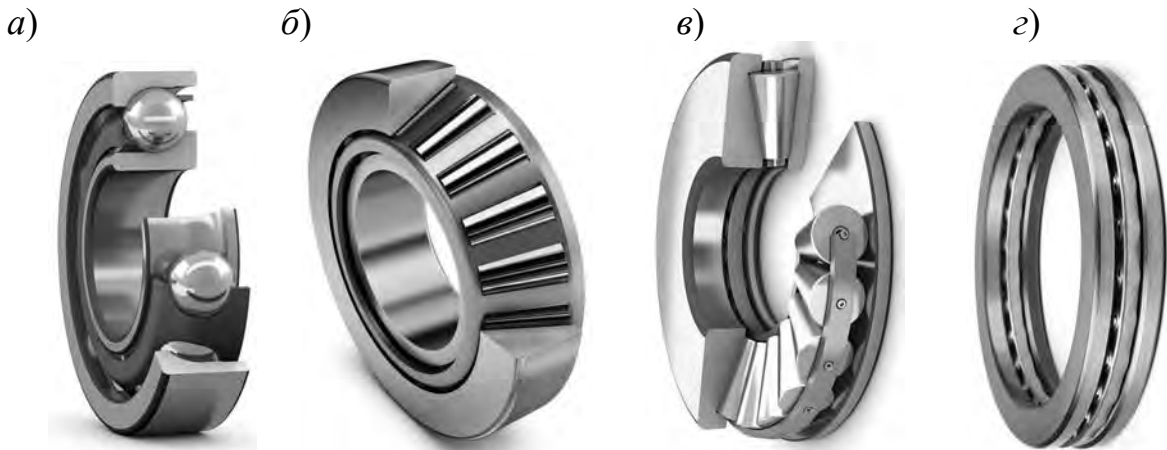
Различные типы подшипников качения: *а* – радиально-упорный шариковый; *б* – радиально-упорный роликовый конический; *в* – упорный шариковый
